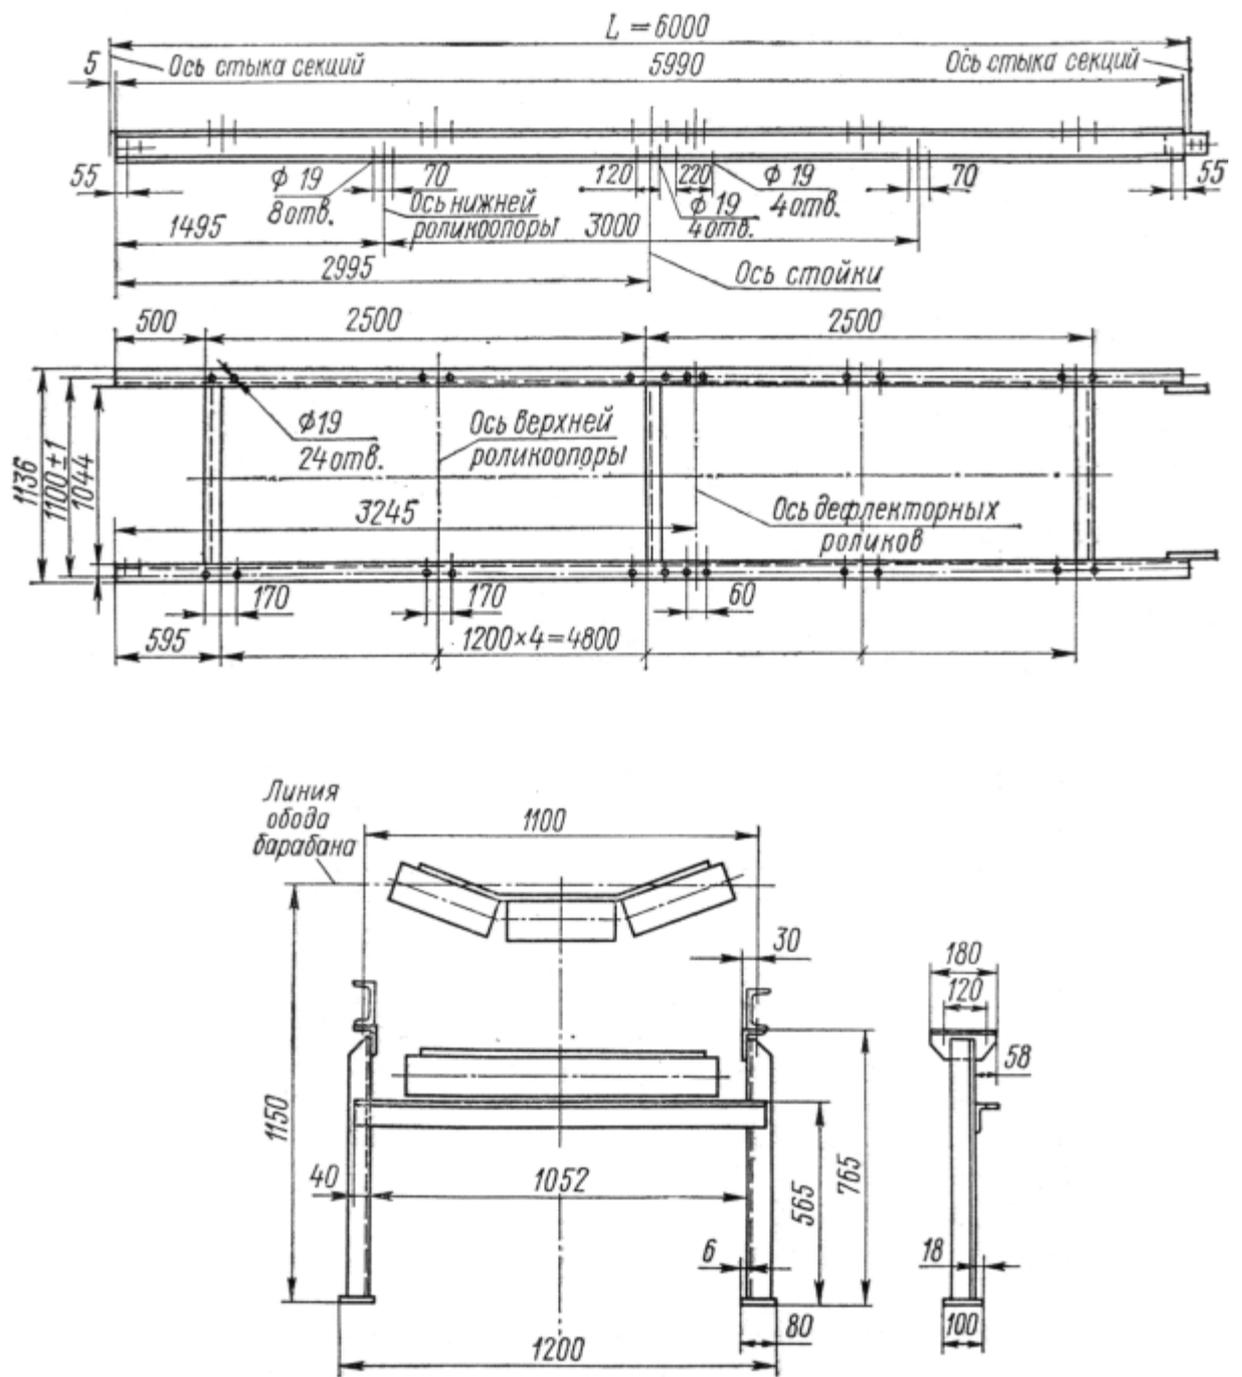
Пример конструкции средней части и стойки средней части ленточного конвейера с шириной ленты 800 мм
